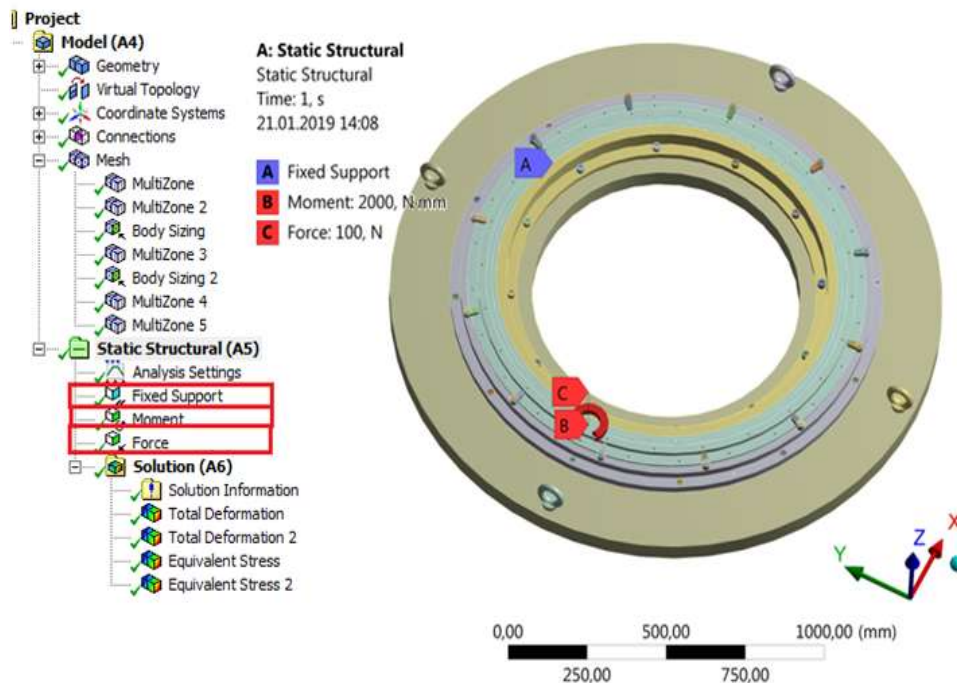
Конечно-элементная модель детали «Кольцо», закрепленной в зажимном приспособлении с приложенными закреплениями и нагрузками
